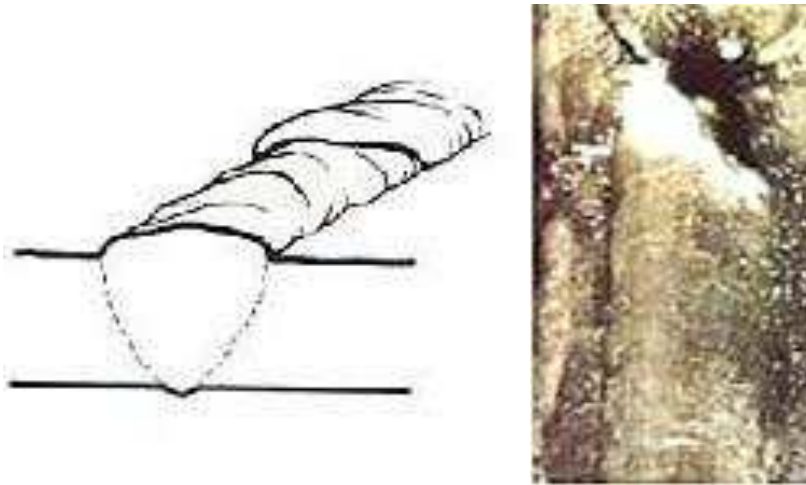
9 *Falta de continuidad en el cordón de soldadura.
